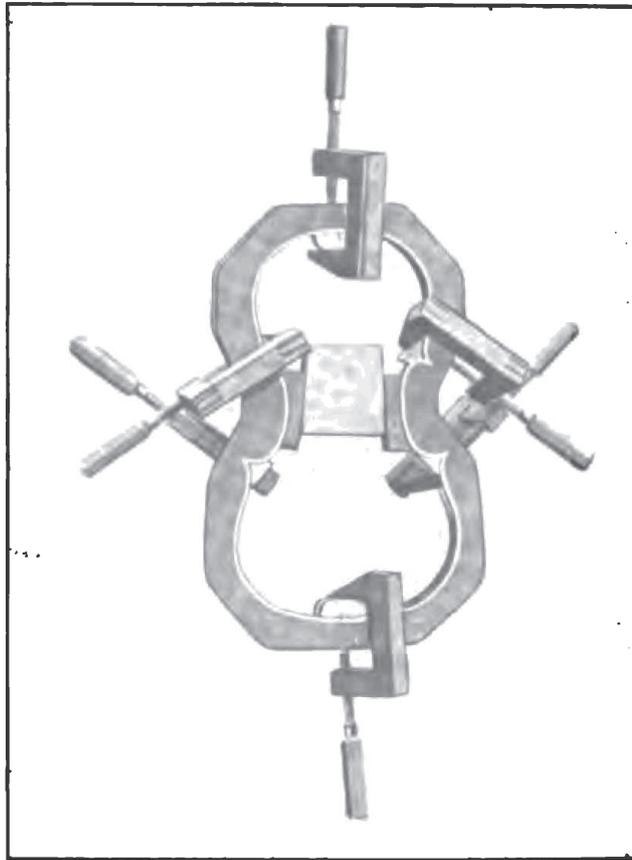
MONTAGE D'UN MOULE EN CREUX OU EN DEDANS.
